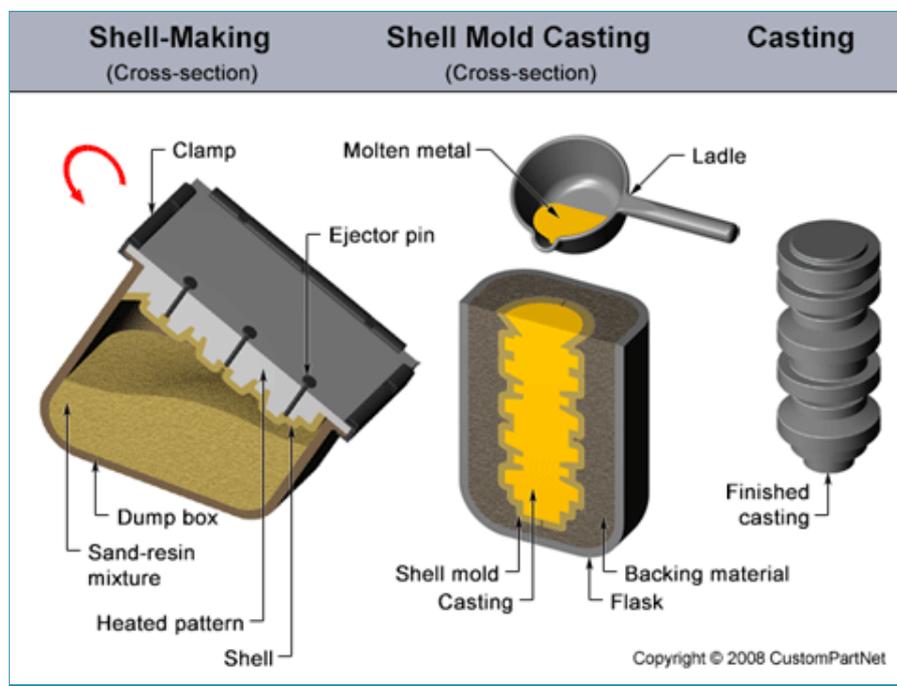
Processo *shell molding*. Fonte: <https://www.custompartnet.com/wu/shell-mold-casting>
